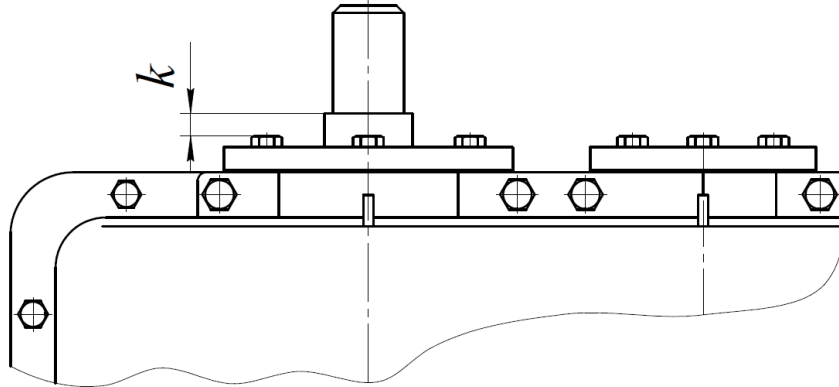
Відстань між корпусом редуктора та обертовою деталлю
